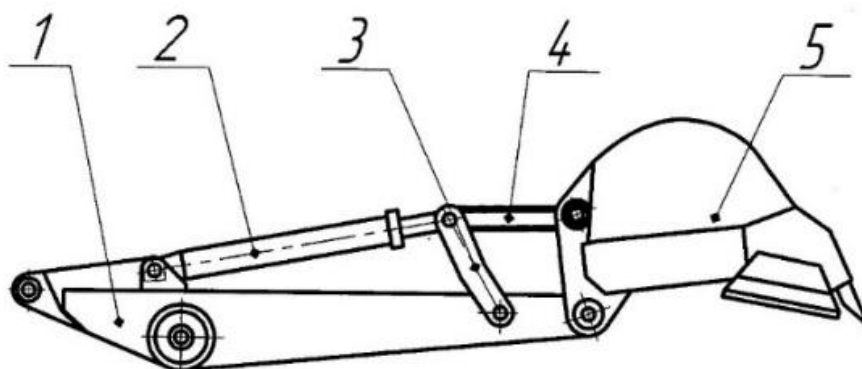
Схема серийной конструкции механизма поворота ковша:
